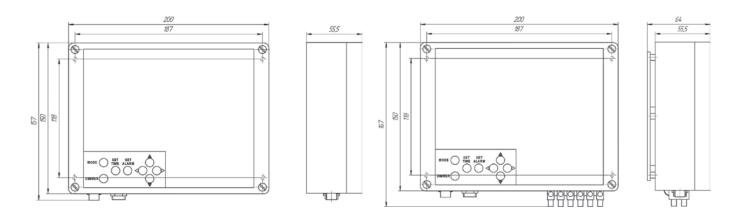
Габаритный чертеж ИПСС-00, ИПСС-01
